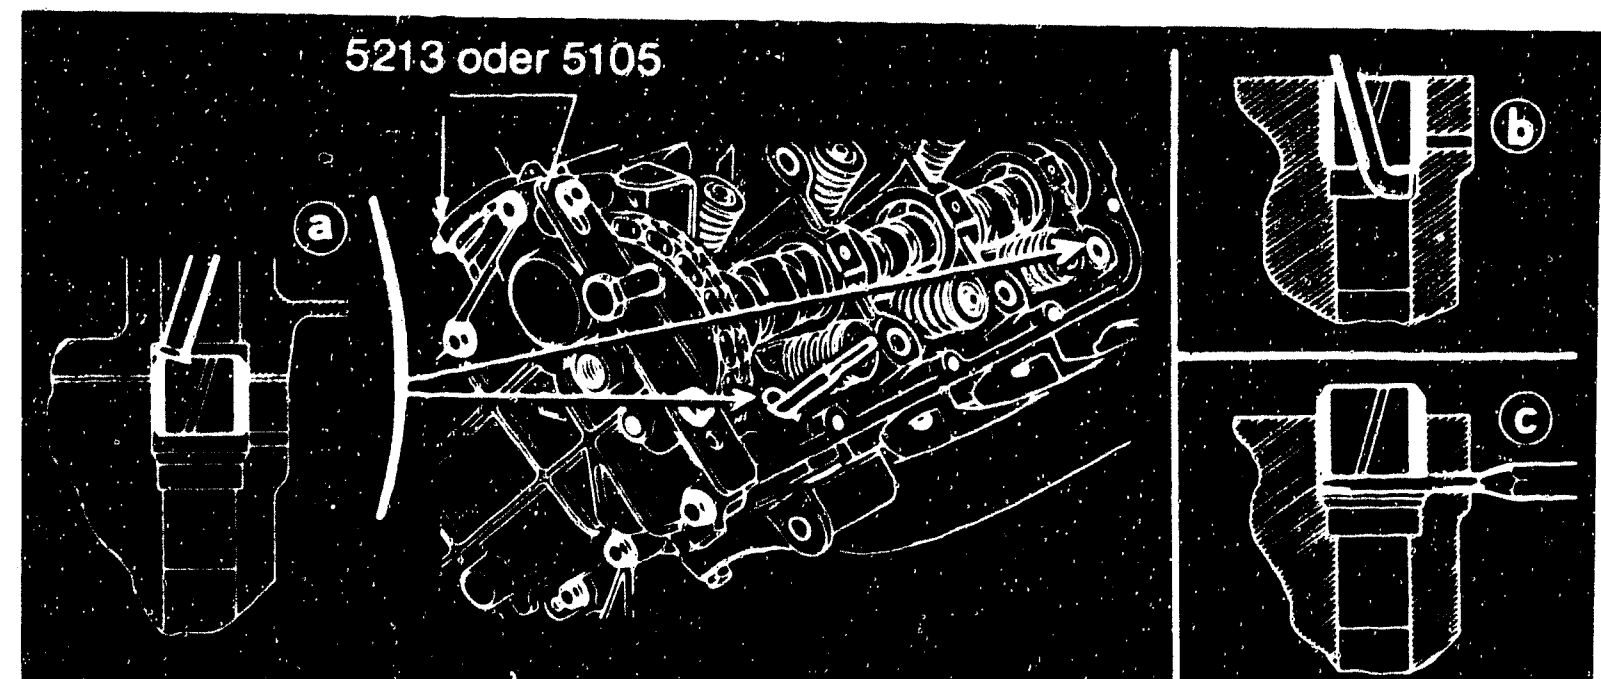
B 28 V6-Motor: Das Nockenwellen-Steuerrad ist vor dem Ausbau des Zylinderkopfs mit dem Spezialwerkzeug 5213 oder 5105 zu fixieren, damit die Kette gespannt bleibt. a) Die beiden Zentrierhülsen sind vor dem Ausbau abzusenken, und vor dem Einbau wieder anzuheben (b) und zu sichern (c).
